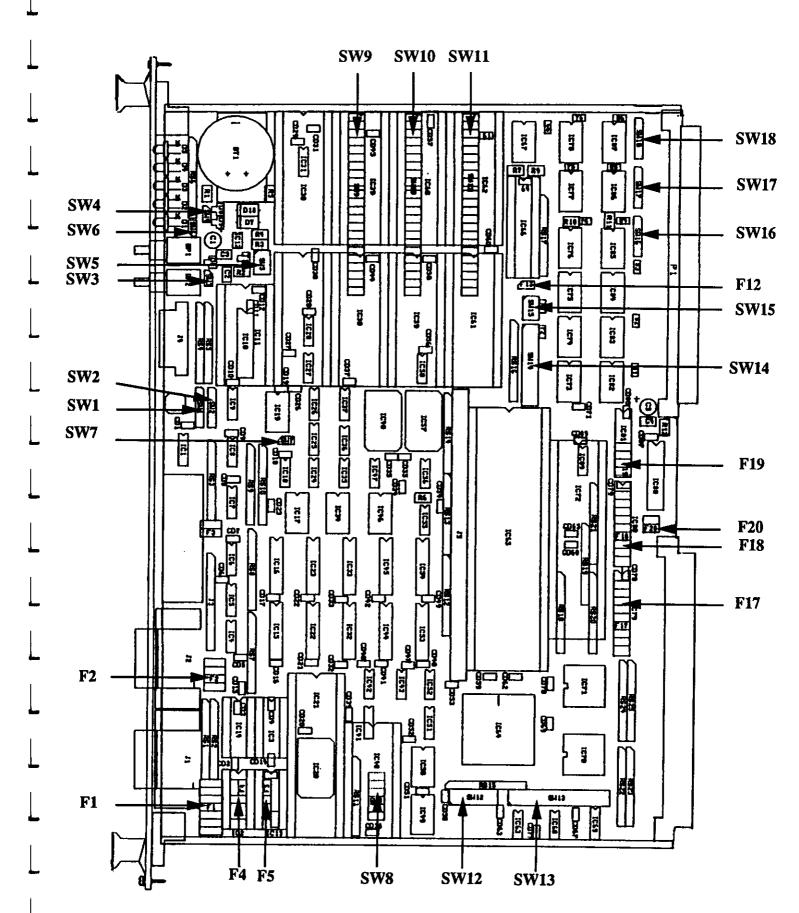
Emplacement des sélecteurs et gouttes de soudure - Face composants
